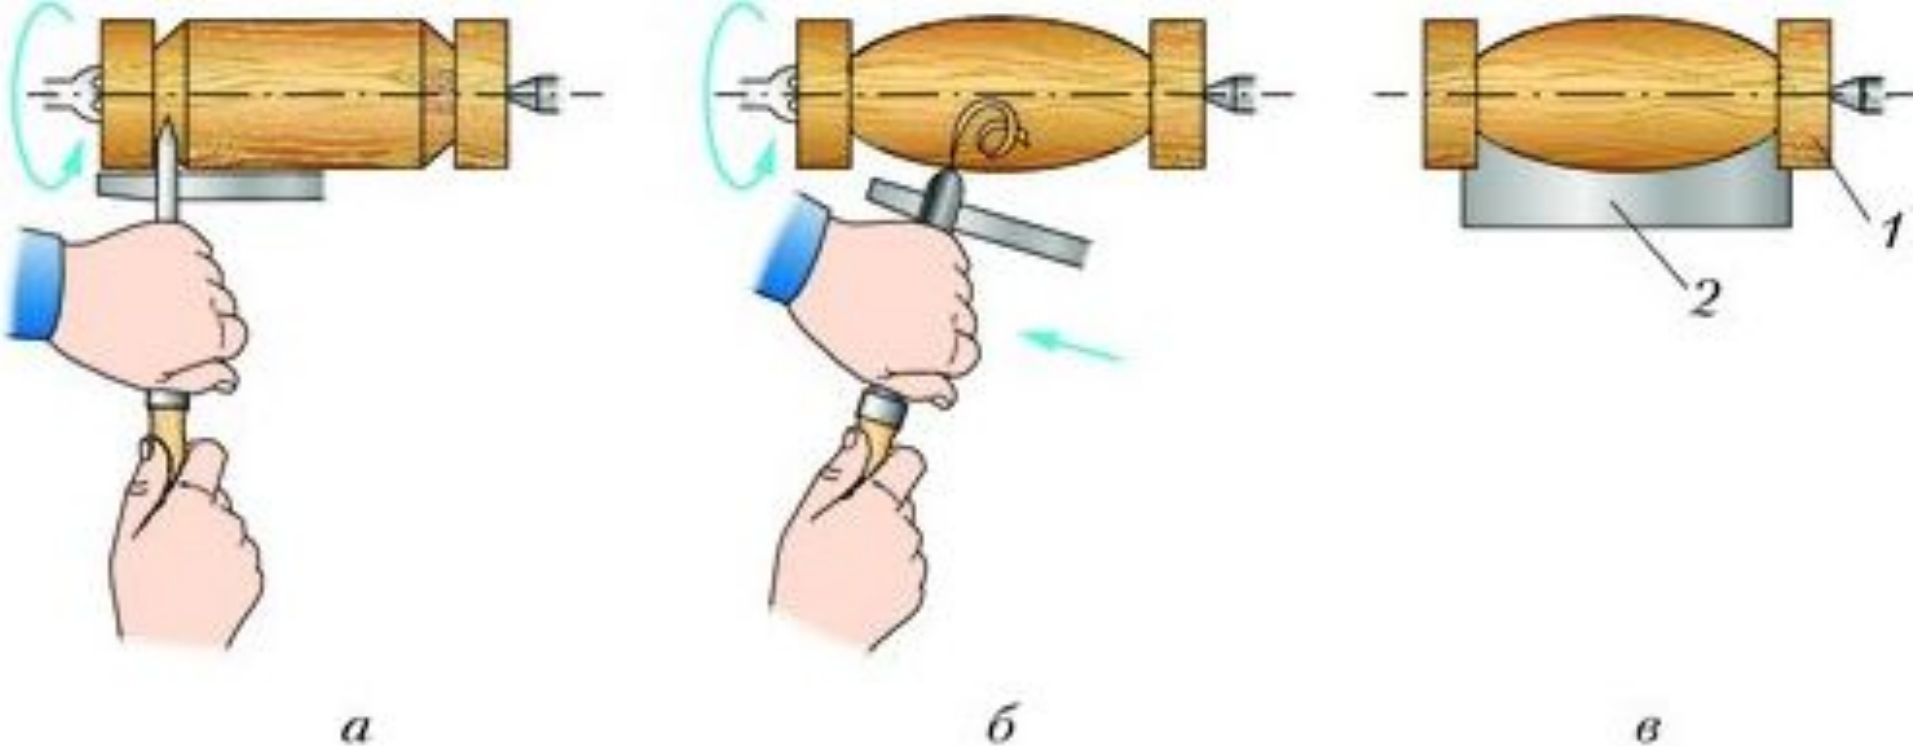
Обработка выпуклой поверхности: *а* – подрезание внутренних торцов; *б* – черновое точение; *в* – проверка формы поверхности шаблоном; 1 – заготовка; 2 – шаблон
